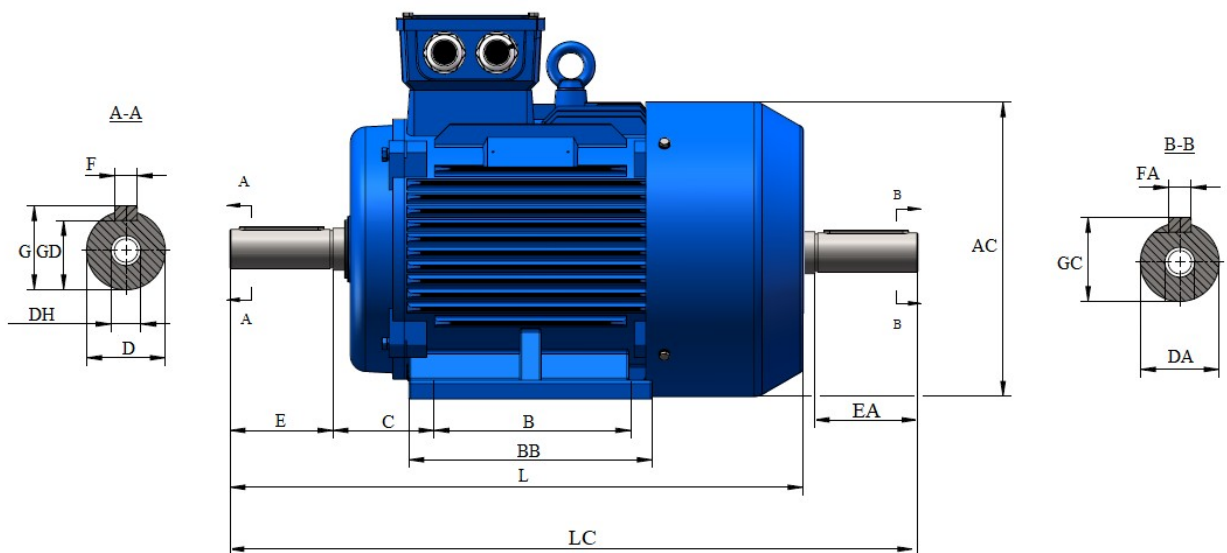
Чертеж электродвигателей с двумя концами вала
